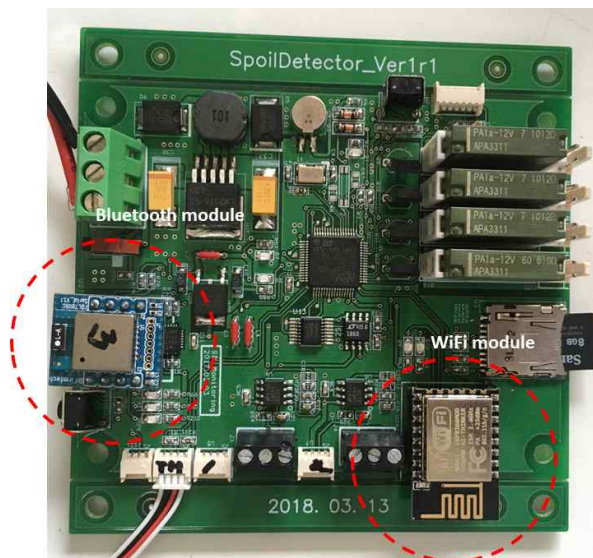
부패감지기 본체의 메인 PCB 무선통신모듈
